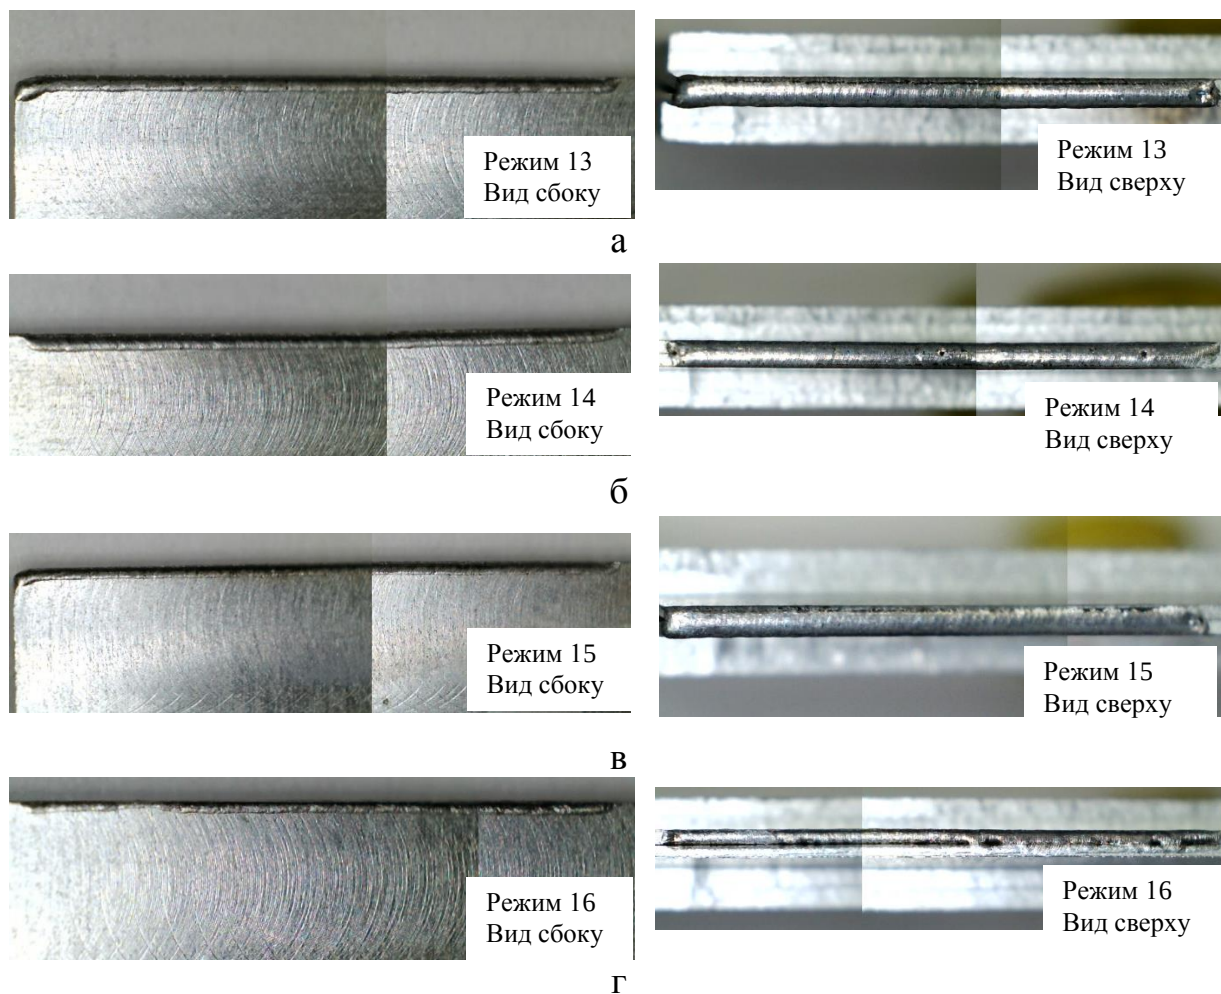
Внешний вид сварных соединений для режимов 13-16
